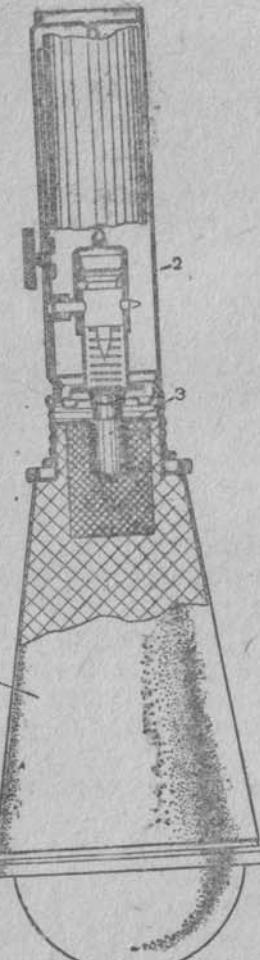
Основные части ручной противотанковой гранаты РПГ-6 (вид в разрезе):
